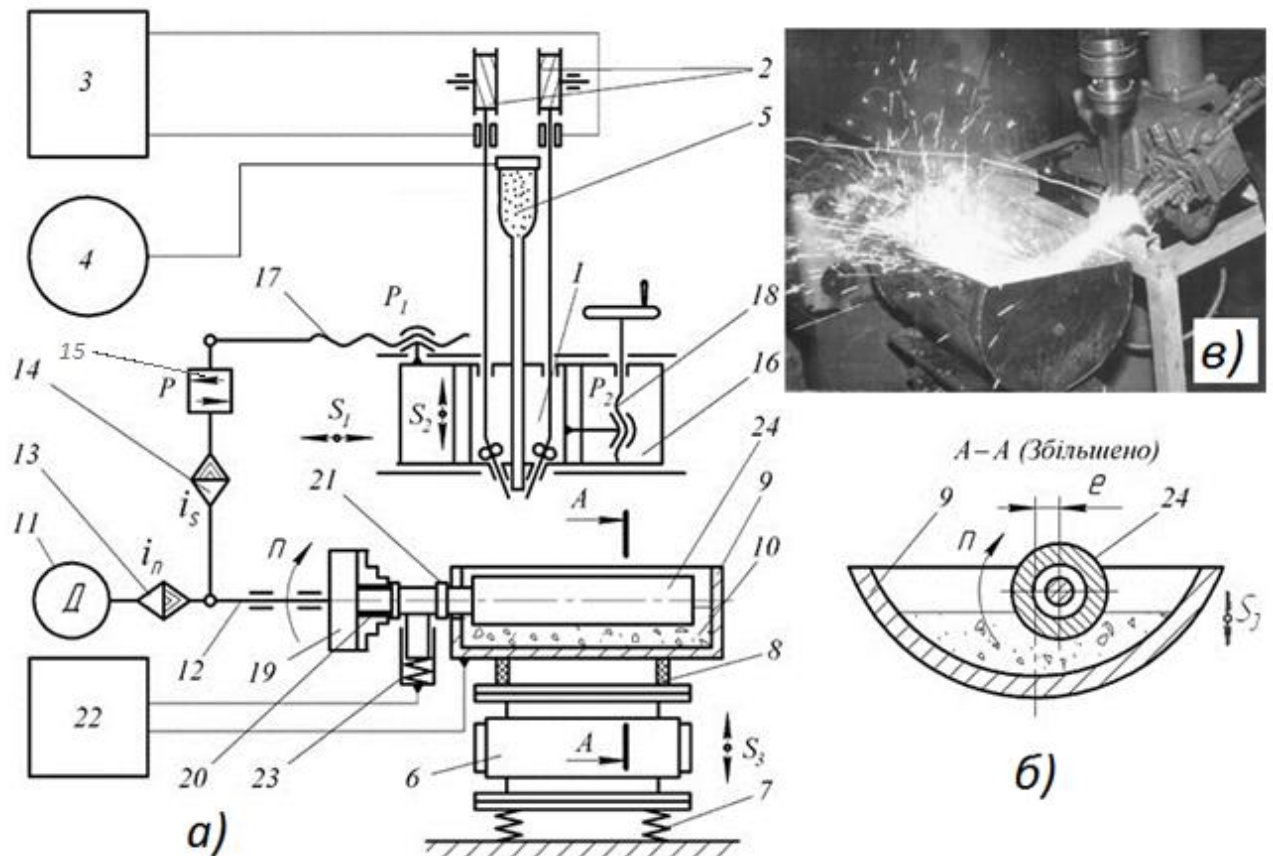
Схема дослідно-промислової установки для формування композиційних покриттів комплексним методом (а), переріз контейнера з деталлю (б) і загальний вигляд робочої зони установки (в):
